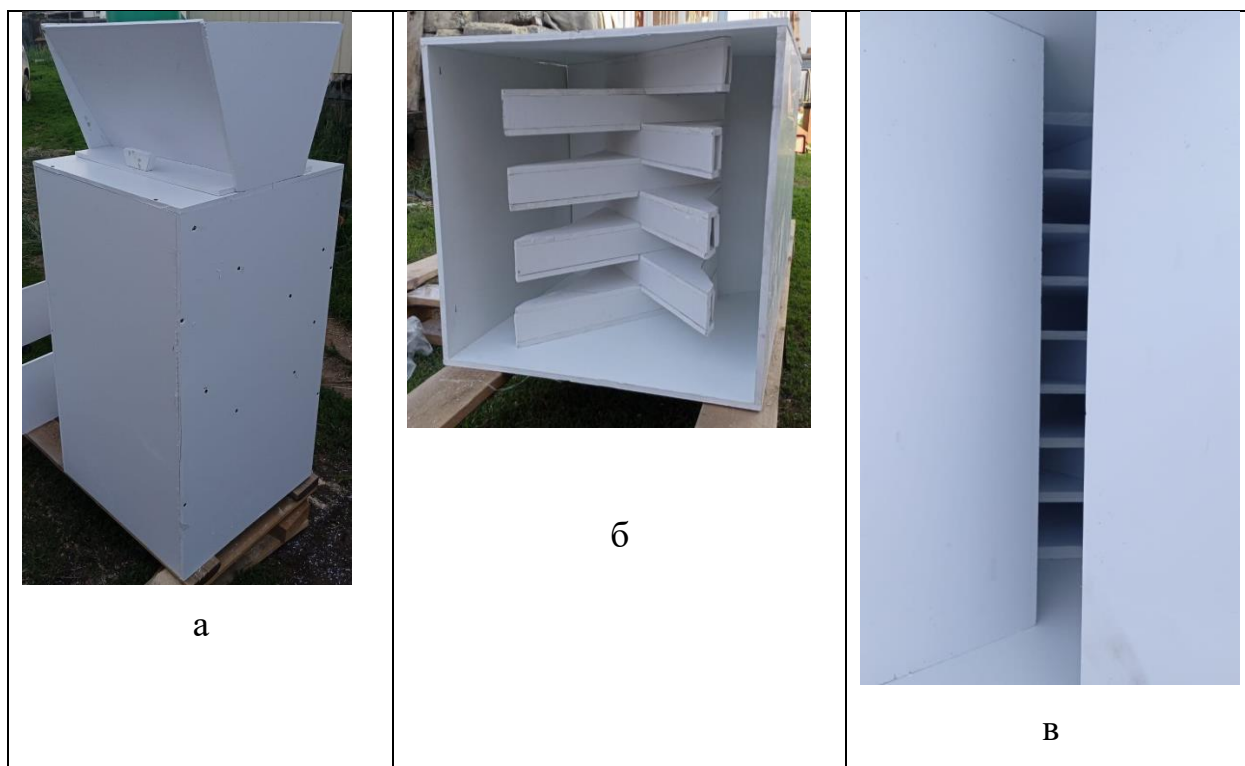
Общий вид установки с делителем семенного потока: а – общий вид установки; б – вид делителя снизу (повернуто); в – вид на делитель сверху (через загрузочный бункер)
